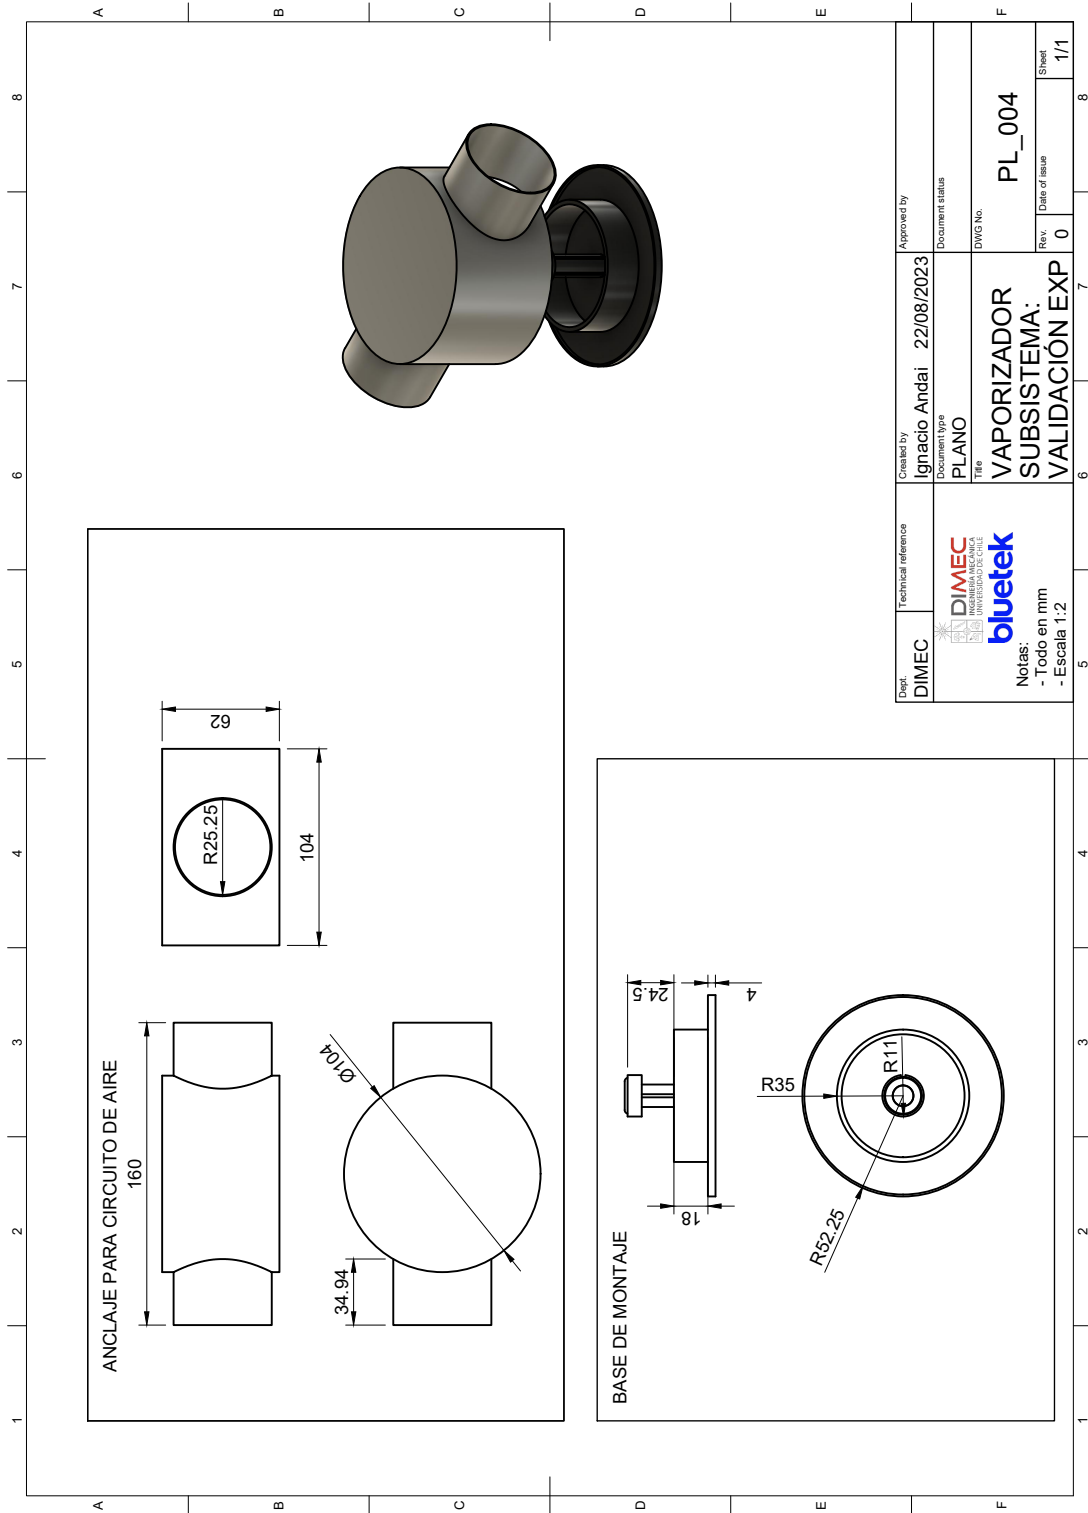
Plano sistema inyección contaminantes. Detalle anclaje y atomizador.
